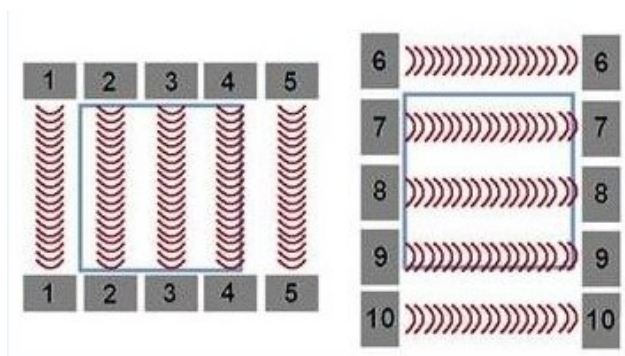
Disposición de los sensores durante la inspección de los refuerzos soldados.
